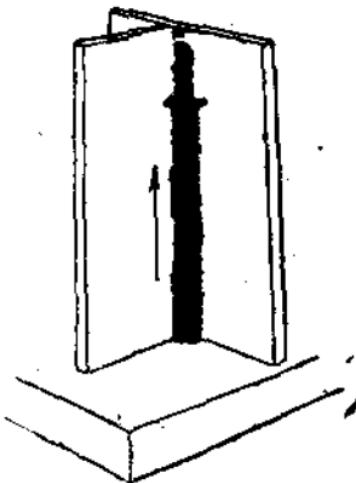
Вертикальная трехслойная сварка для сосудов под давление.
